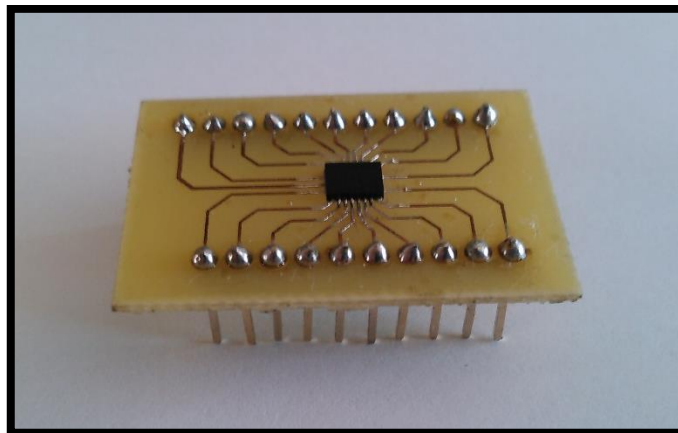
PCB del zócalo para el chip bq51050B (vista inclinada)
